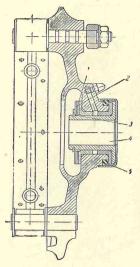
Передняя рычажная вилка: 1-траверса: 2-мостик; 3-овальная несушая труба вилки; 4-реактивный рычаг переднего тормоза; 5-наколечник вилки.
